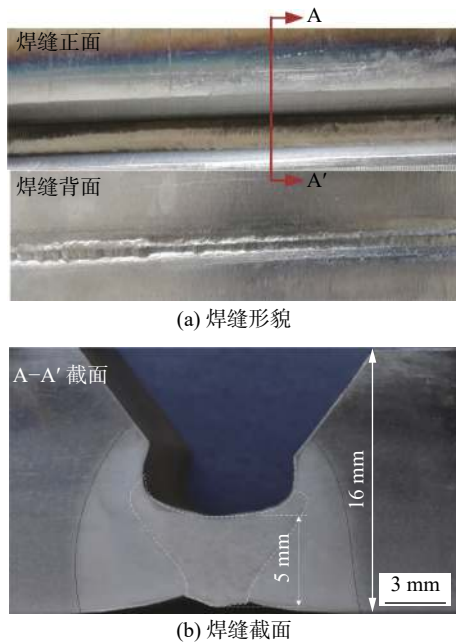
直流叠加脉冲型 TIG 焊缝成形
